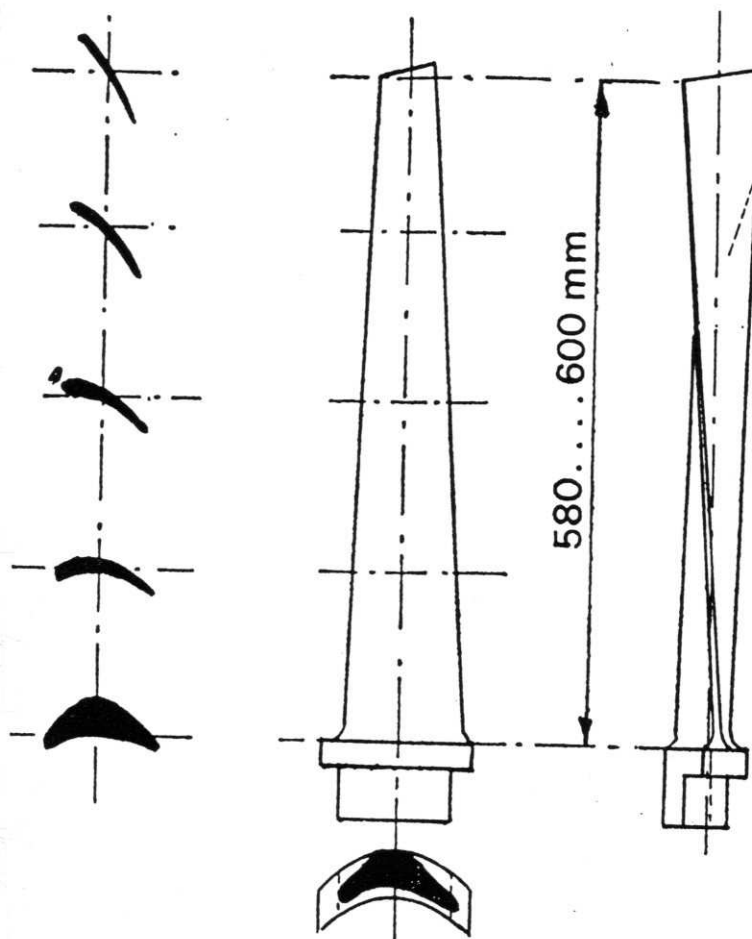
Vrillage et différentes sections d'une pale basse-pression.
